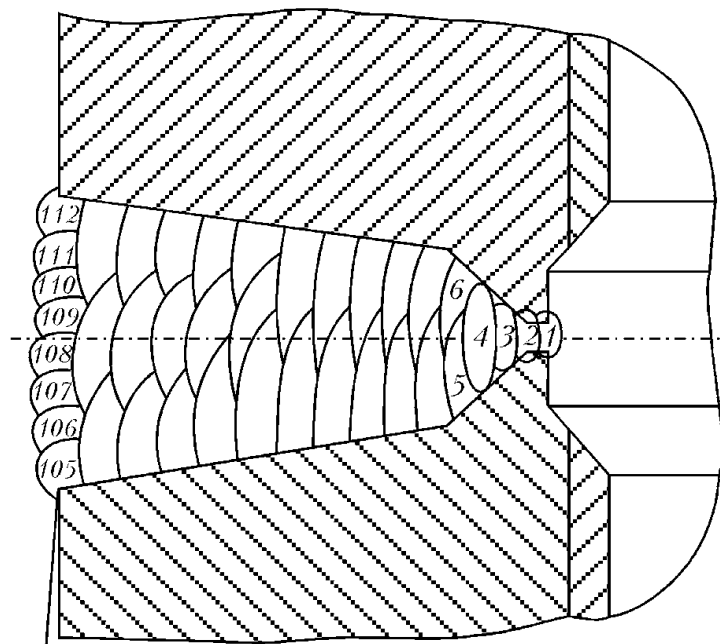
Схема стандартной разделки кромок сварных соединений, полученных способом ААрДС неплавящимся электродом с применением сварочной проволоки
